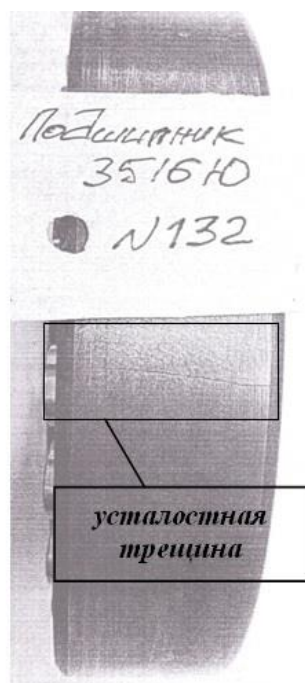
Разрушение внешнего кольца подшипника качения из стали 95Х18Ш
